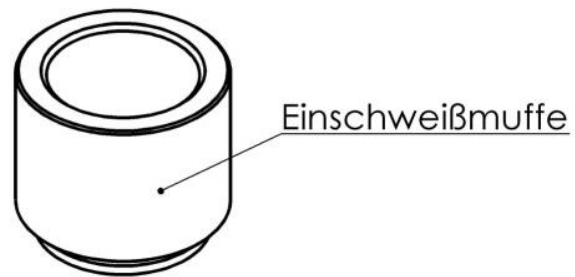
Einschweiß-Montageteil (Schweißmuffe)
